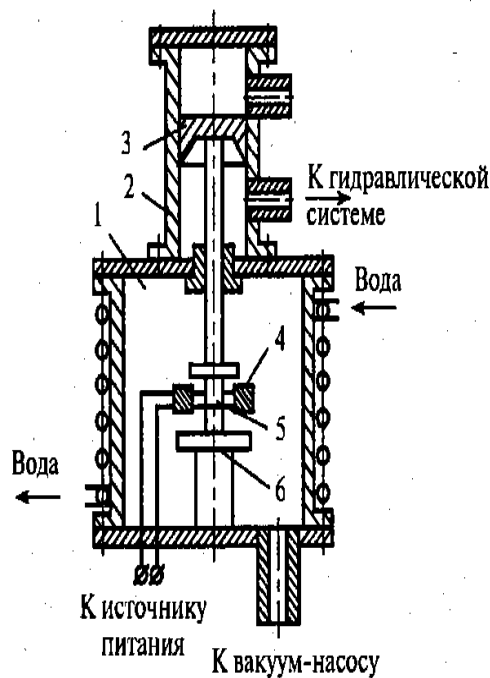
Принципиальная схема установки для диффузионной сварки в вакууме:
